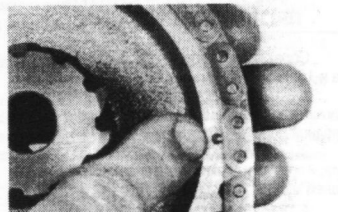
Сцепите звездочку распредвала и приводную цепь таким образом, чтобы метка на звездочке располагалась прямо напротив пластины цепи
